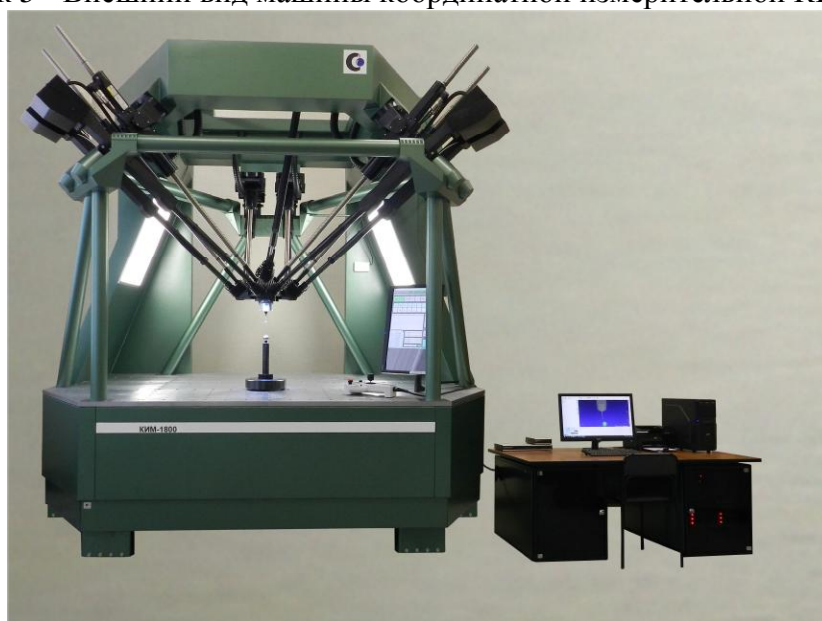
Внешний вид машины координатной измерительной КИМ-1800
